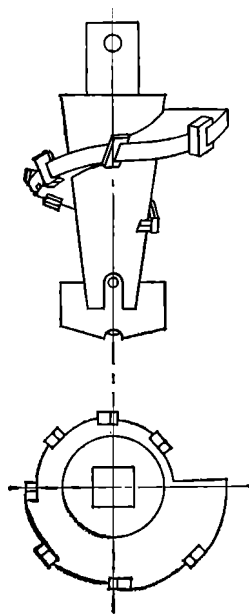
Шнековый бур конструкции треста Укр-гидроспецфундаментстрой.
